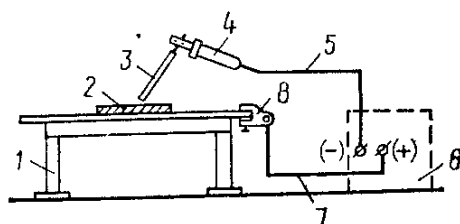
Схема поста для ручной дуговой сварки:
